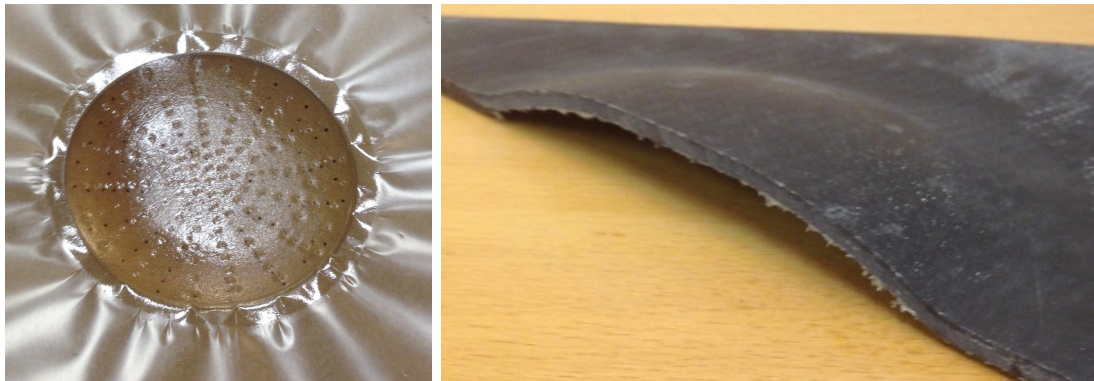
Links: thermogeformte und anschließend perforierte Thermoplastlage auf Formwerkzeug, rechts: Querschnitt des fertigen Bauteils
